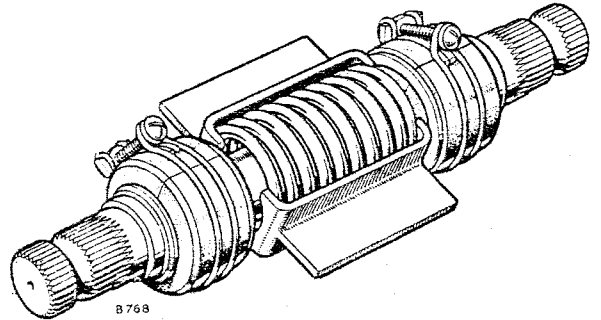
Montaje del conjunto del eje-compensador de la dirección.
